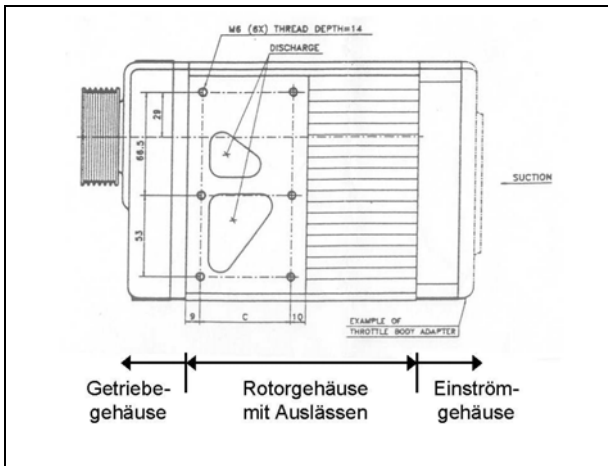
Gesamtzeichnung des als Basismaschine verwendeten Opcon-Autorotor OA2076 Schraubensladers [16]
